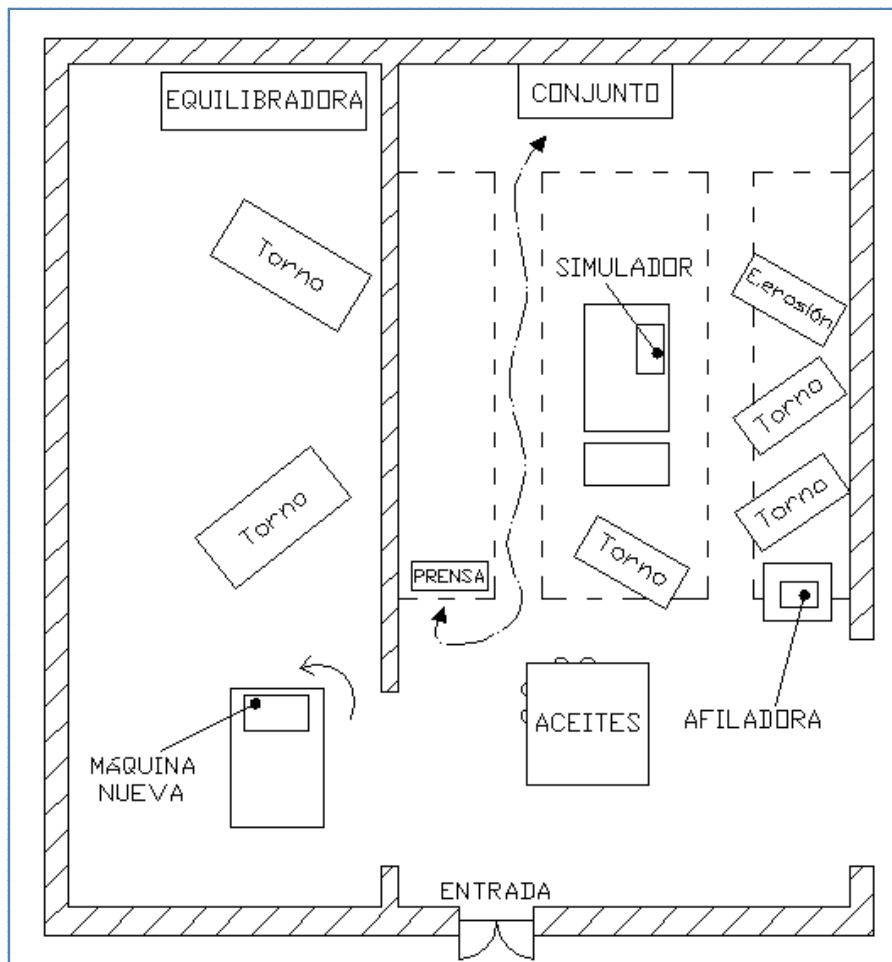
Croquis en planta de la 3ª distribución de zonas propuesta
